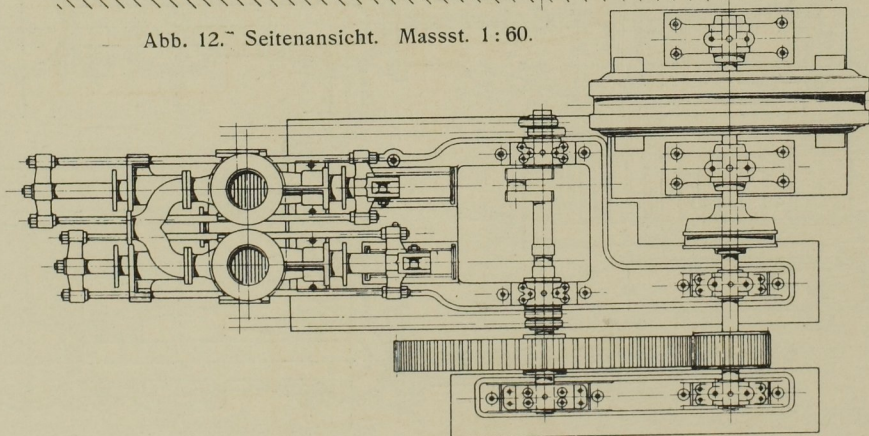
Grundriss der Pumpmaschine. Massst. 1:60.
